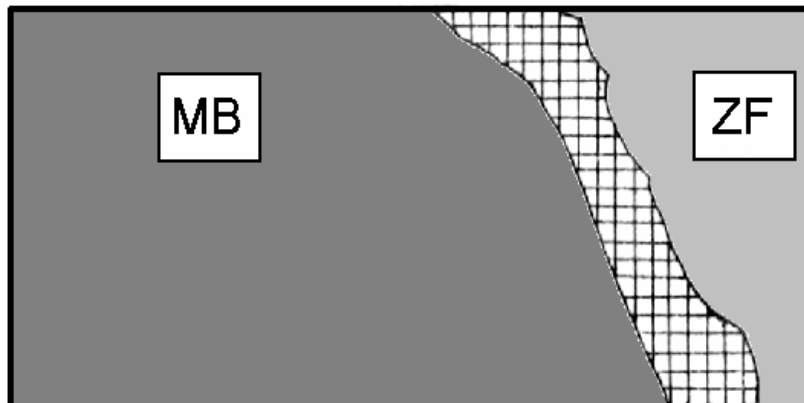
Maillage de la ZAT pour la soudure initiale (S1)
